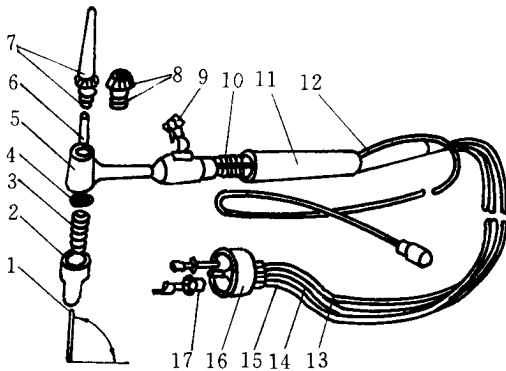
QS—85°/250 型水冷式 TIG 焊炬分解图
